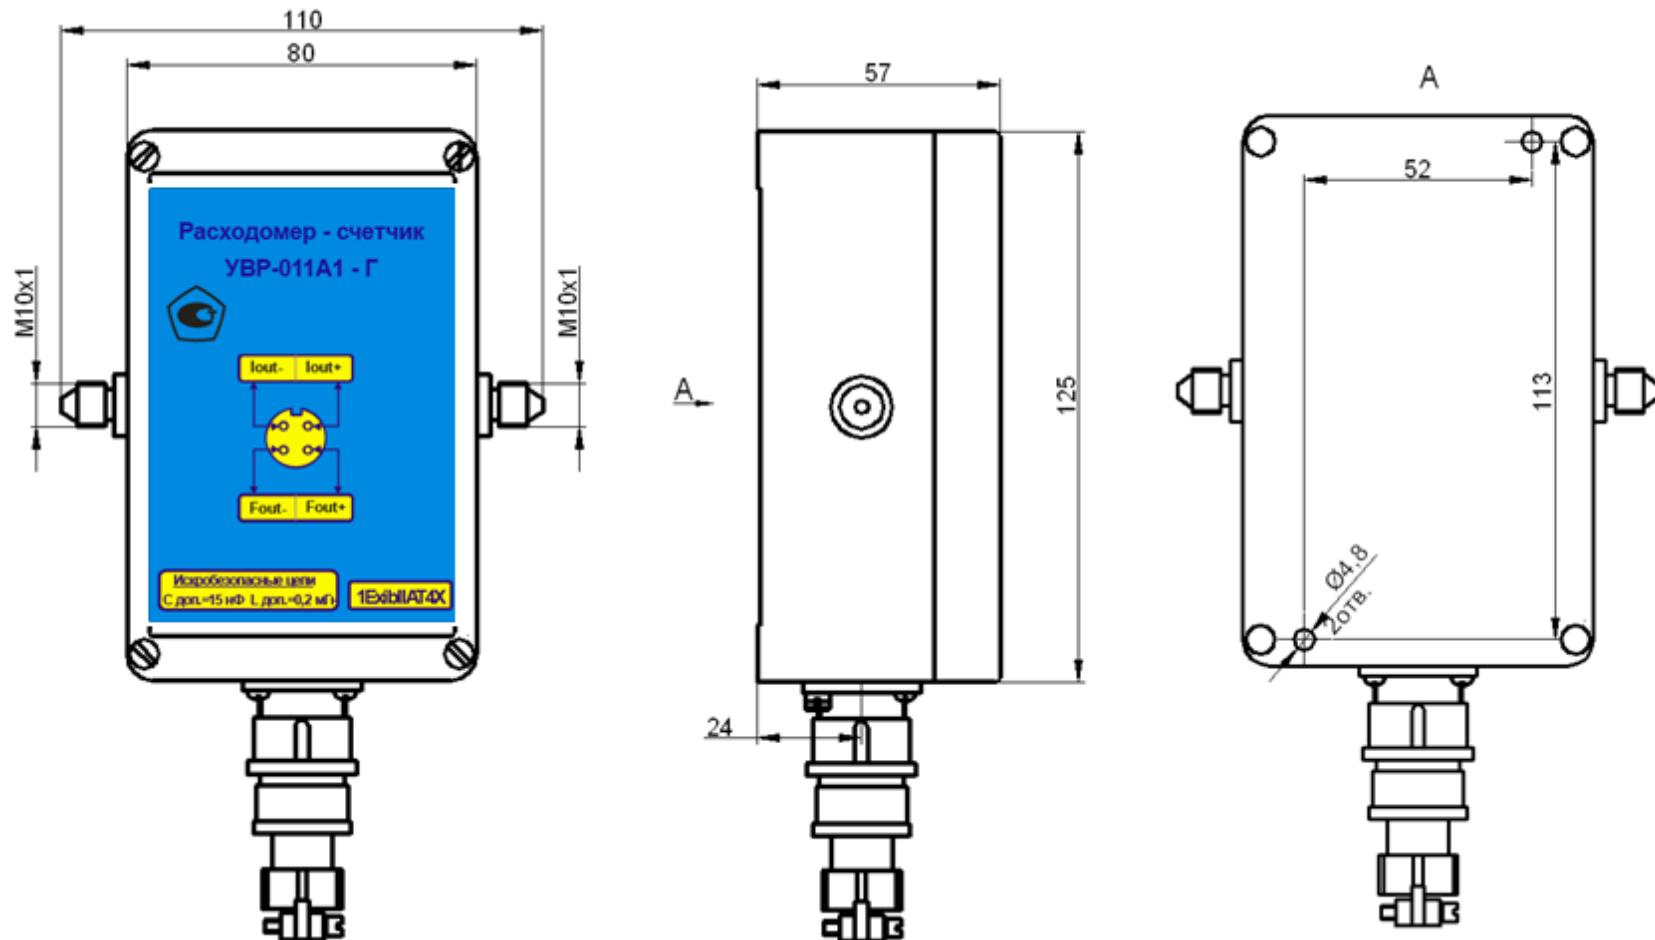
Внешний вид, габаритные и установочные размеры БЭ
